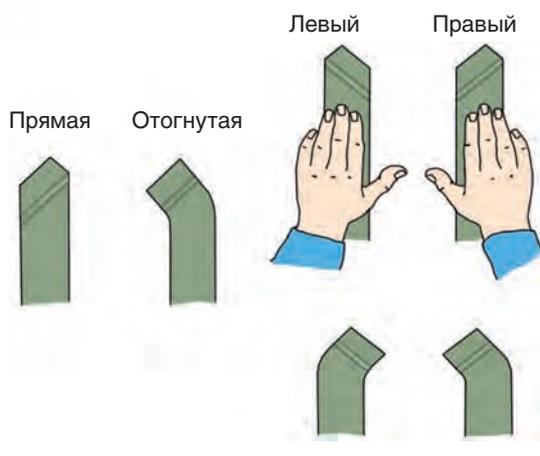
Виды токарных резцов по форме головки (слева) и направлению подачи (справа)
